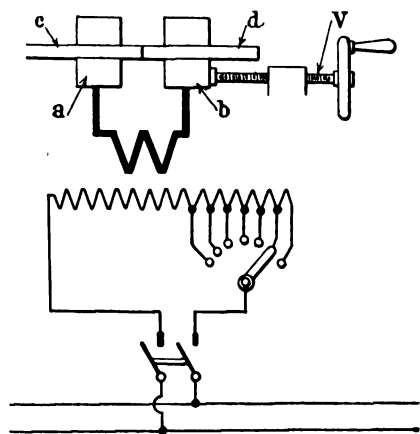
Principe du procédé Thomson pour la soudure électrique par résistance.
